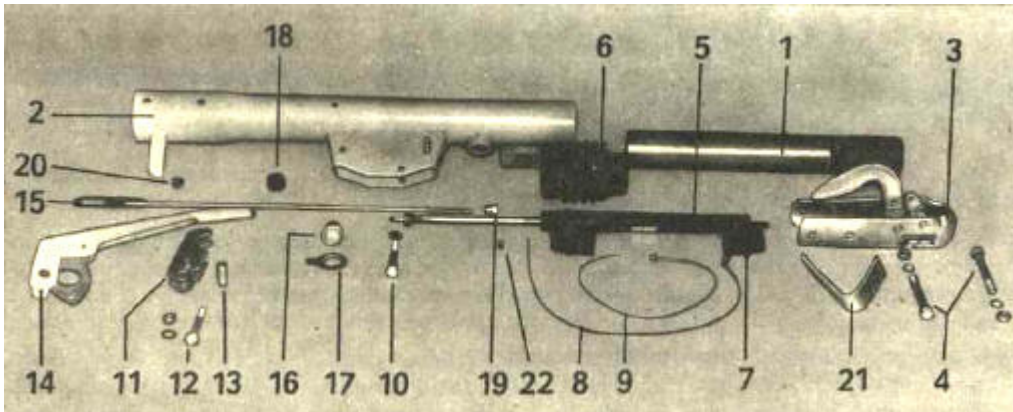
Schubstück der mechanischen Auflaufbremse
